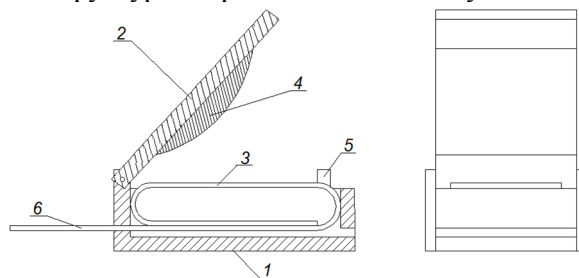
Структура плоского з'єднувача: 1 – корпус; 2 – рухлива планка у вигляді кришки; 3 – матриця контактів; 4 – ущільнювач; 5 – фіксатор; 6 – зовнішній вивід матриці
